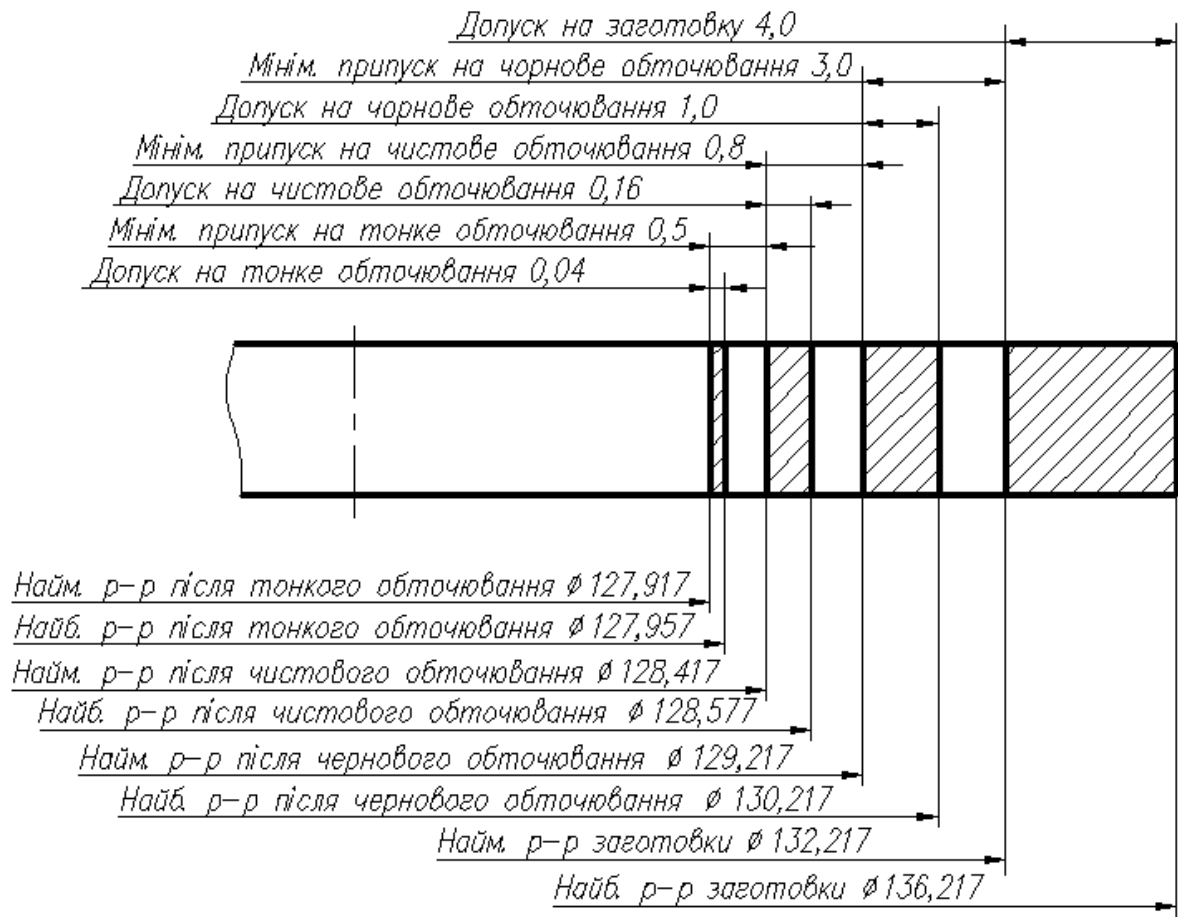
Схема розташування припусків та допусків при обробці поверхні головки $\phi 128f7 \begin{pmatrix} -0,043 \\ -0,083 \end{pmatrix}$.
